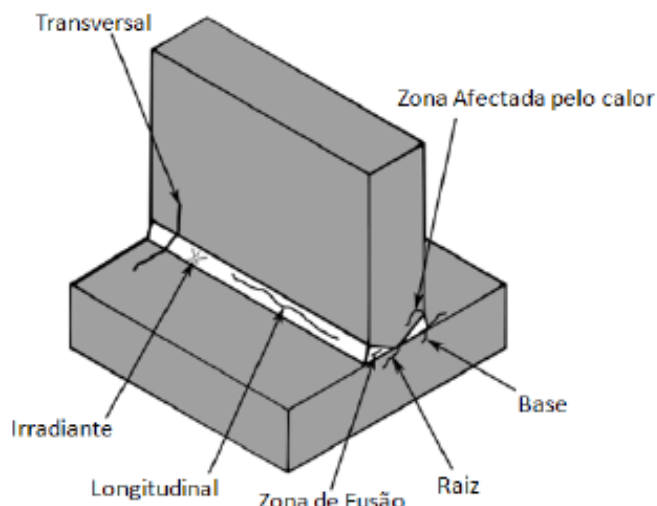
junta soldada apresentando trincas nos cordões de solda
